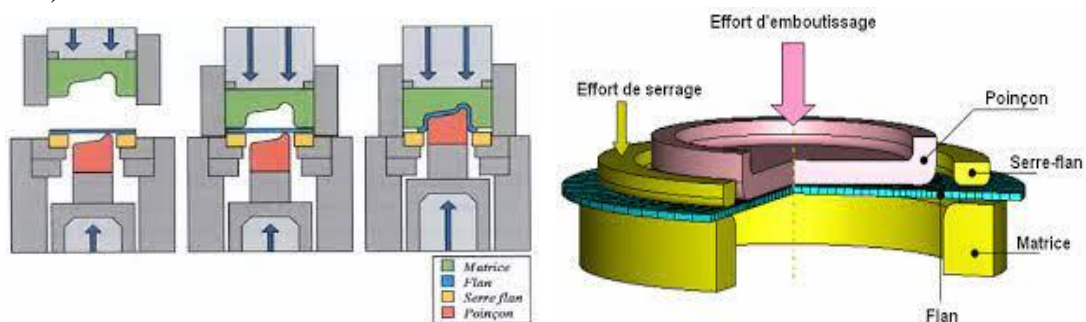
Principe d'emboutissage (pièces forgées) .
